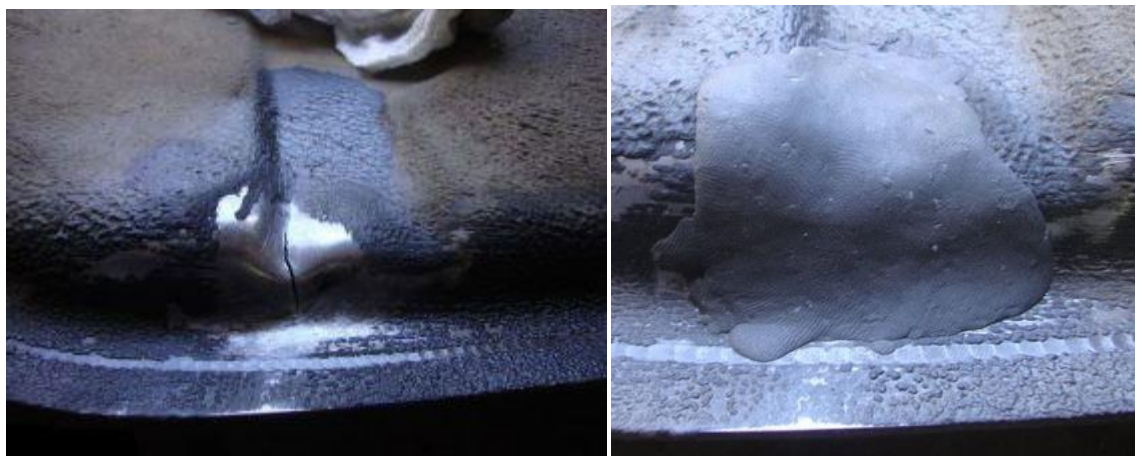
Ремонт бака "холодною зваркою"
